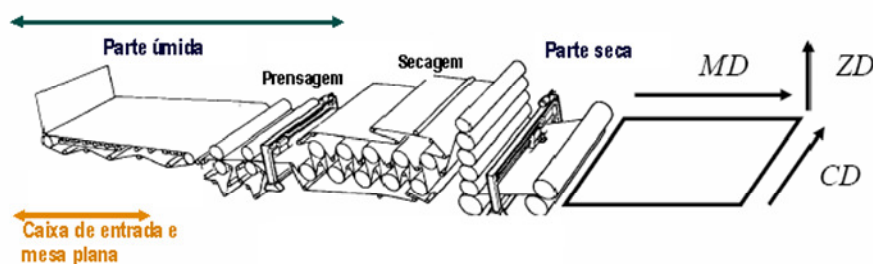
Etapas da fabricação de papel – máquina com mesa plana<sup>5</sup>.
